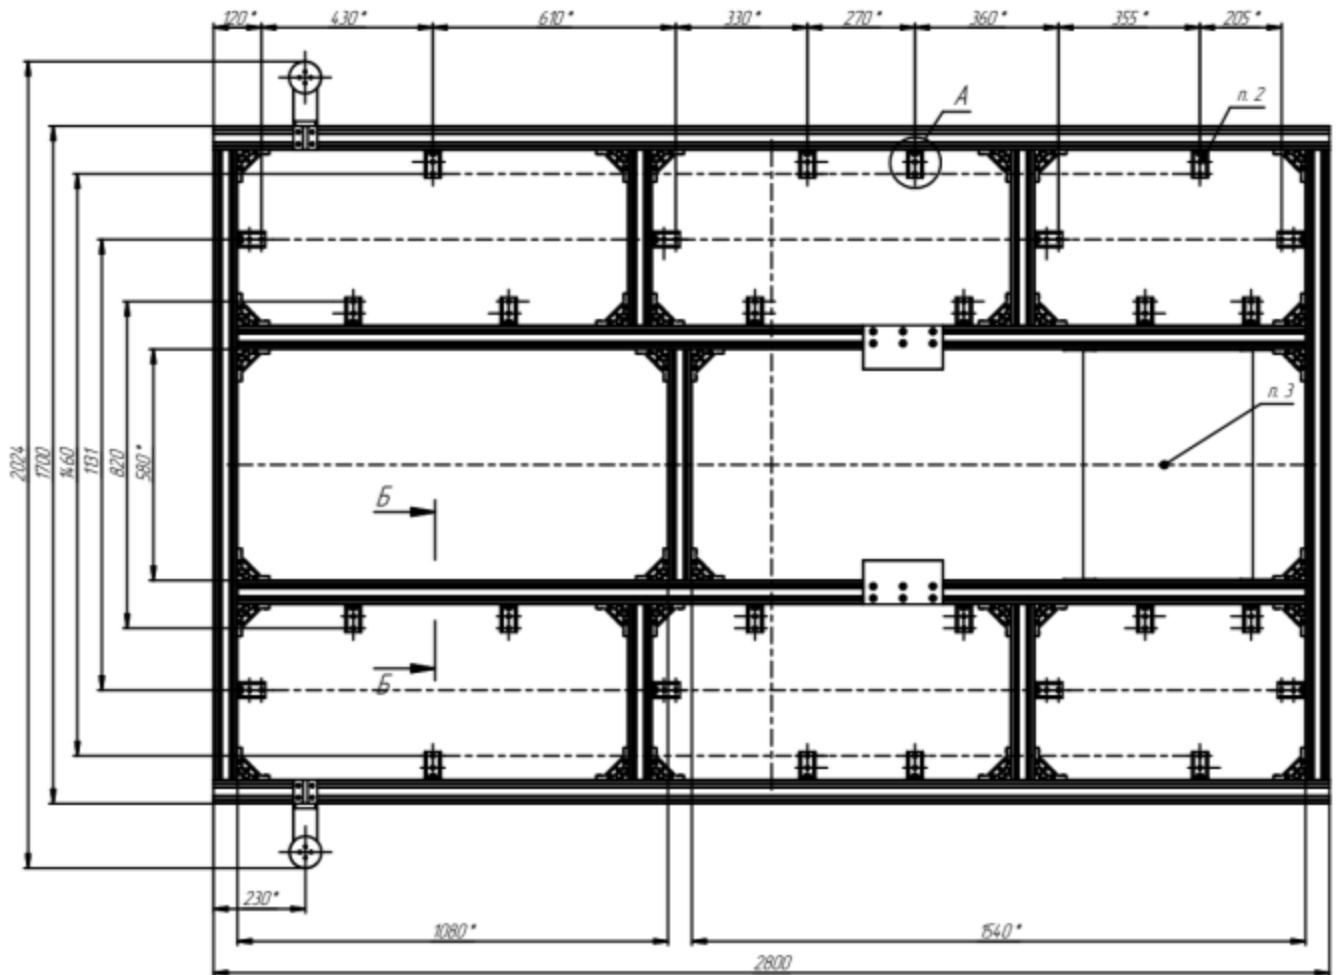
Габаритный чертеж опорной площадки
